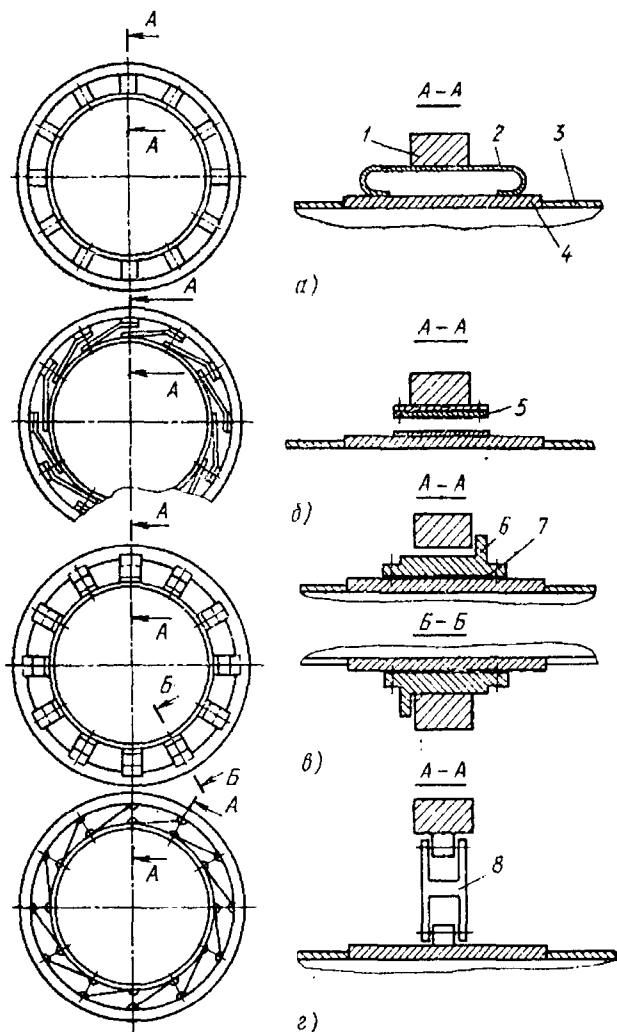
Типы компенсаторов: 1 – бандаж; 2 – эллиптический компенсатор; 3 – обечайка барабана; 4 – подбандажная плита; 5 – тангенциальный компенсатор; 6 – опорный башмак; 7 – регулировочные прокладки; 8 – шарнирный компенсатор.
